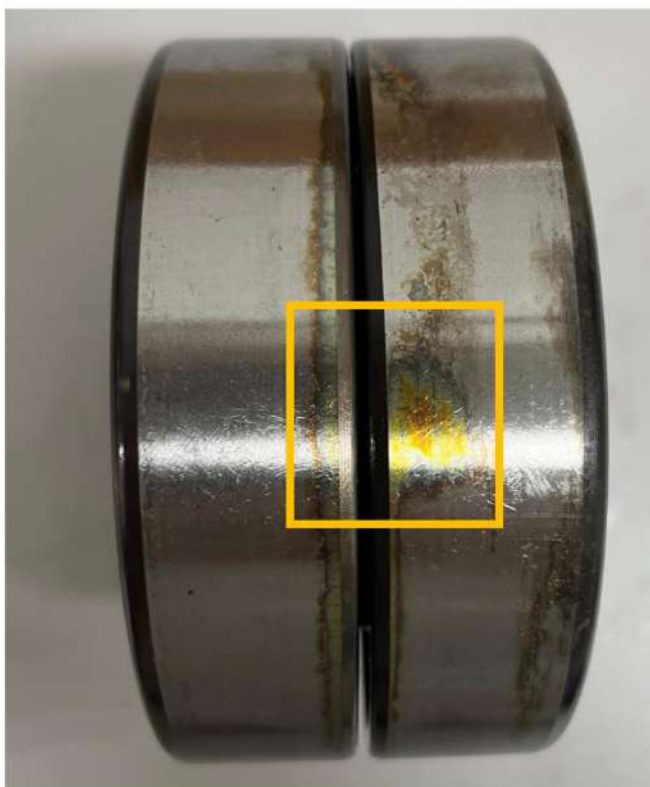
Rolamento SKF 7311 BECBP: Inspeção Visual
